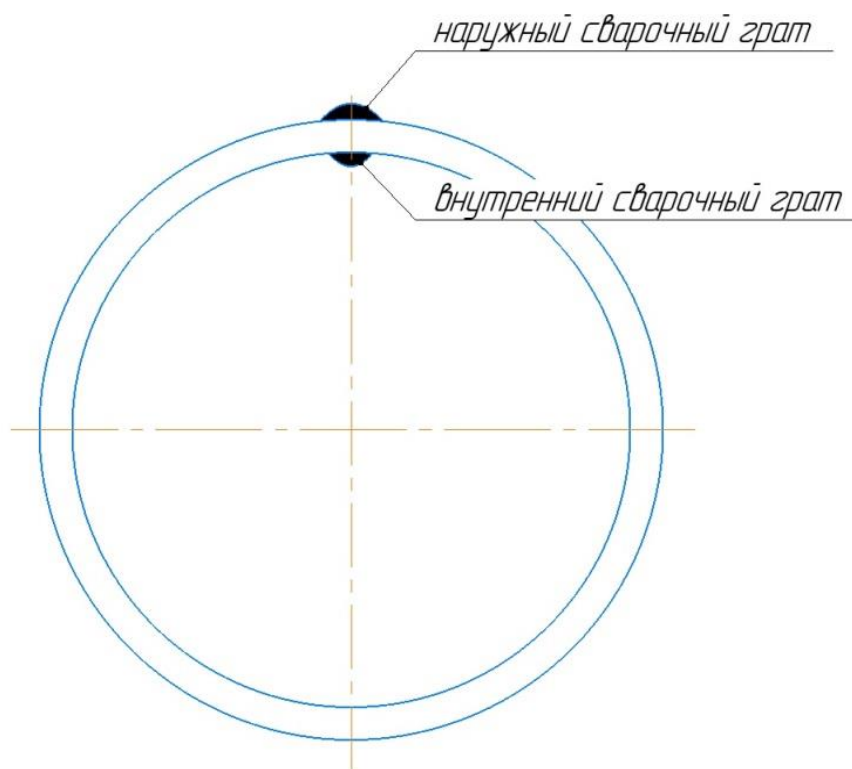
Наружный и внутренний сварочный грат
